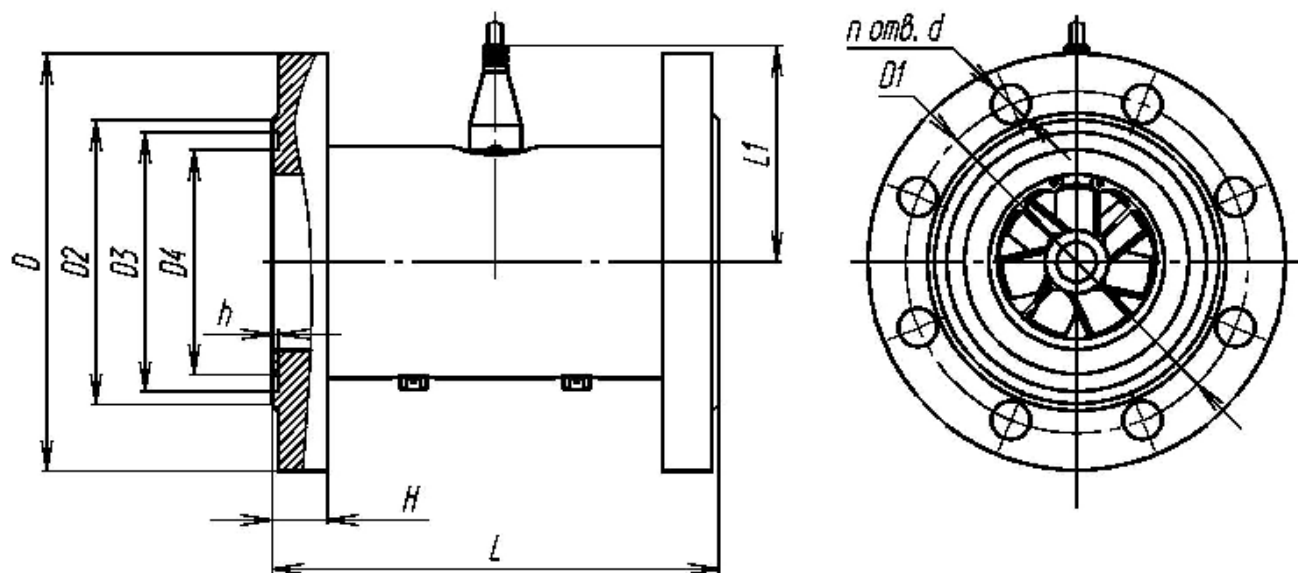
Габаритные и присоединительные размеры расходомера-счётчика с фланцевым присоединением
